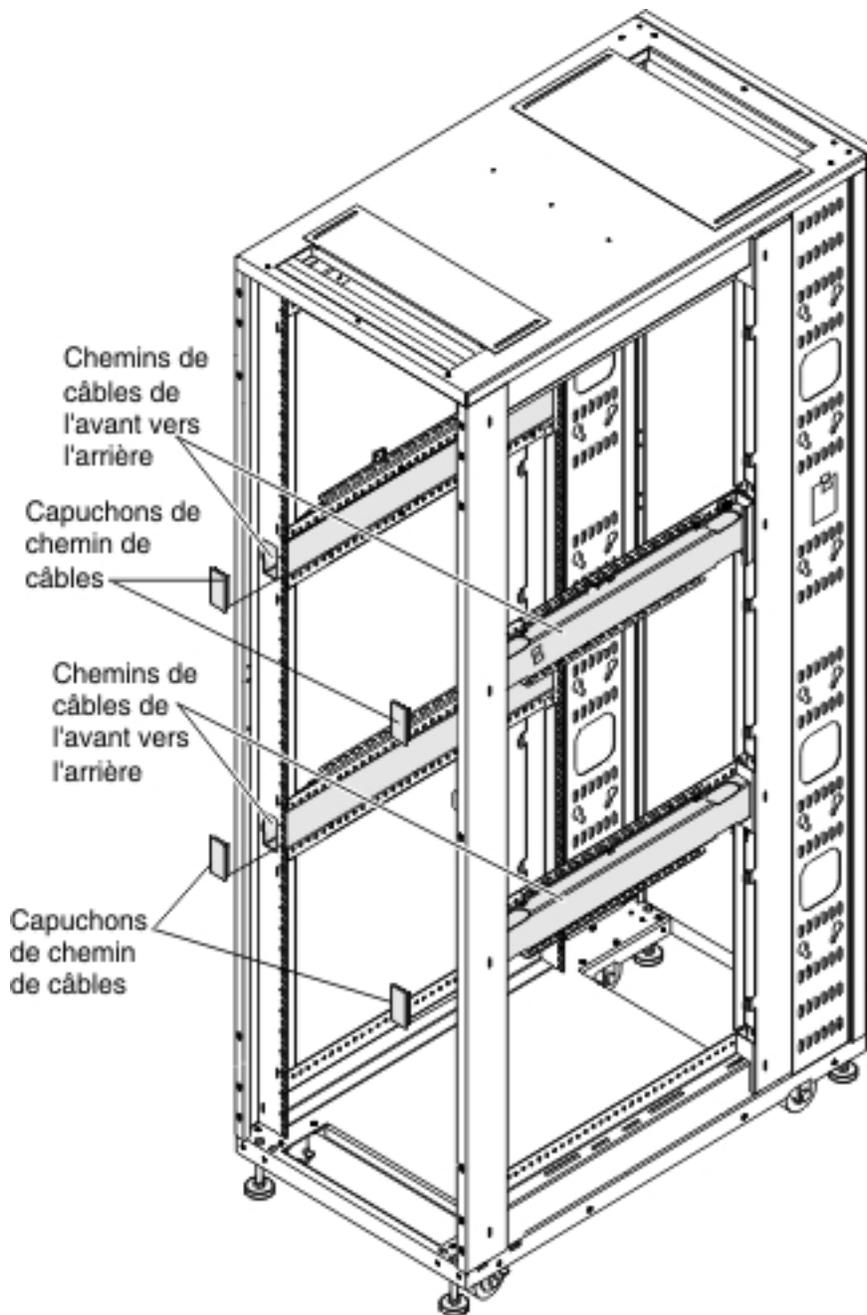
Retrait des caches des chemins de câbles de l'avant vers l'arrière
